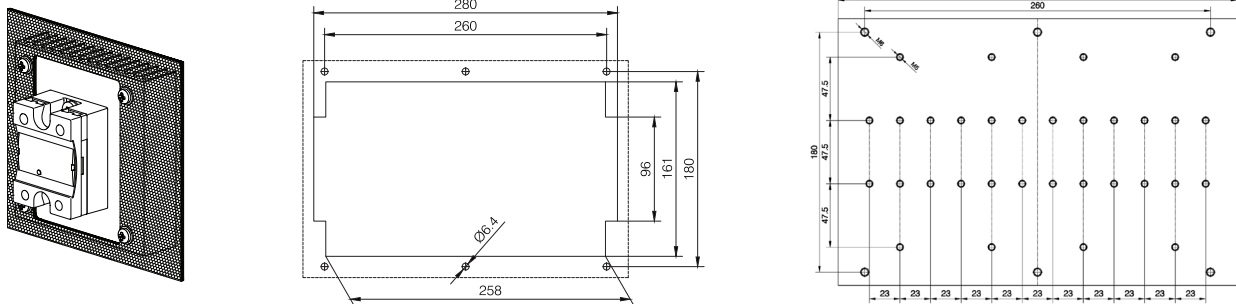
Position der Befestigungsbohrungen für die Montage durch die Schaltschrankrückwand.
